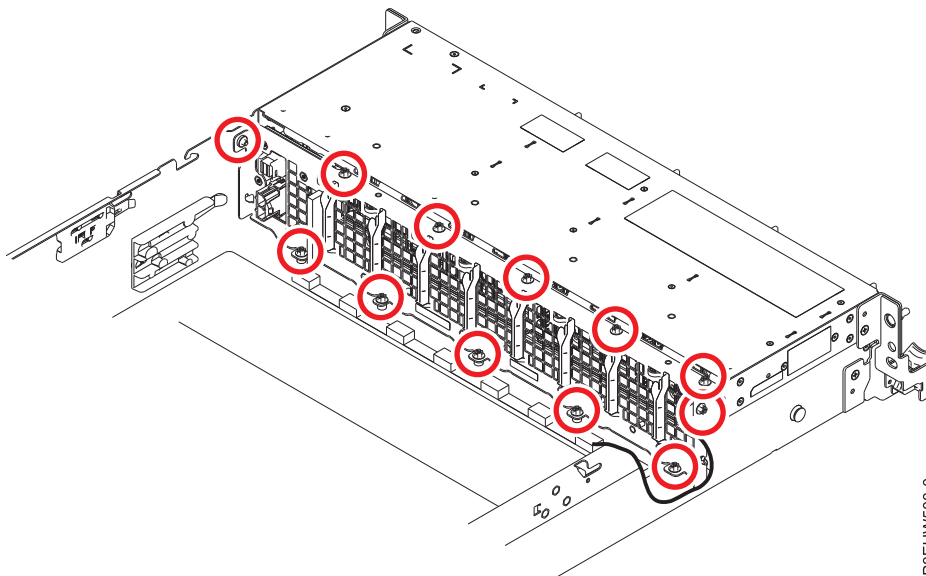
Emplacements des vis de la carte de ventilateur d'unité de disque
